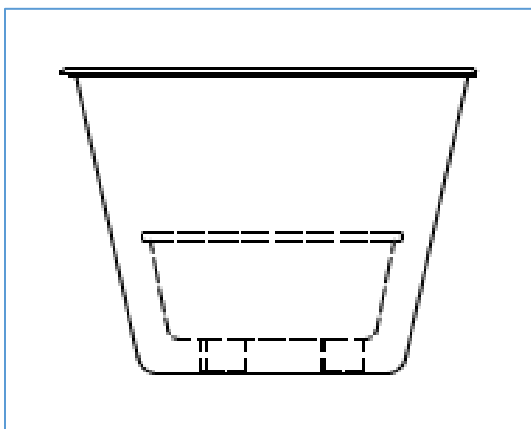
Construcción e implementación de la cámara de fermentación del AutoBioGen.
